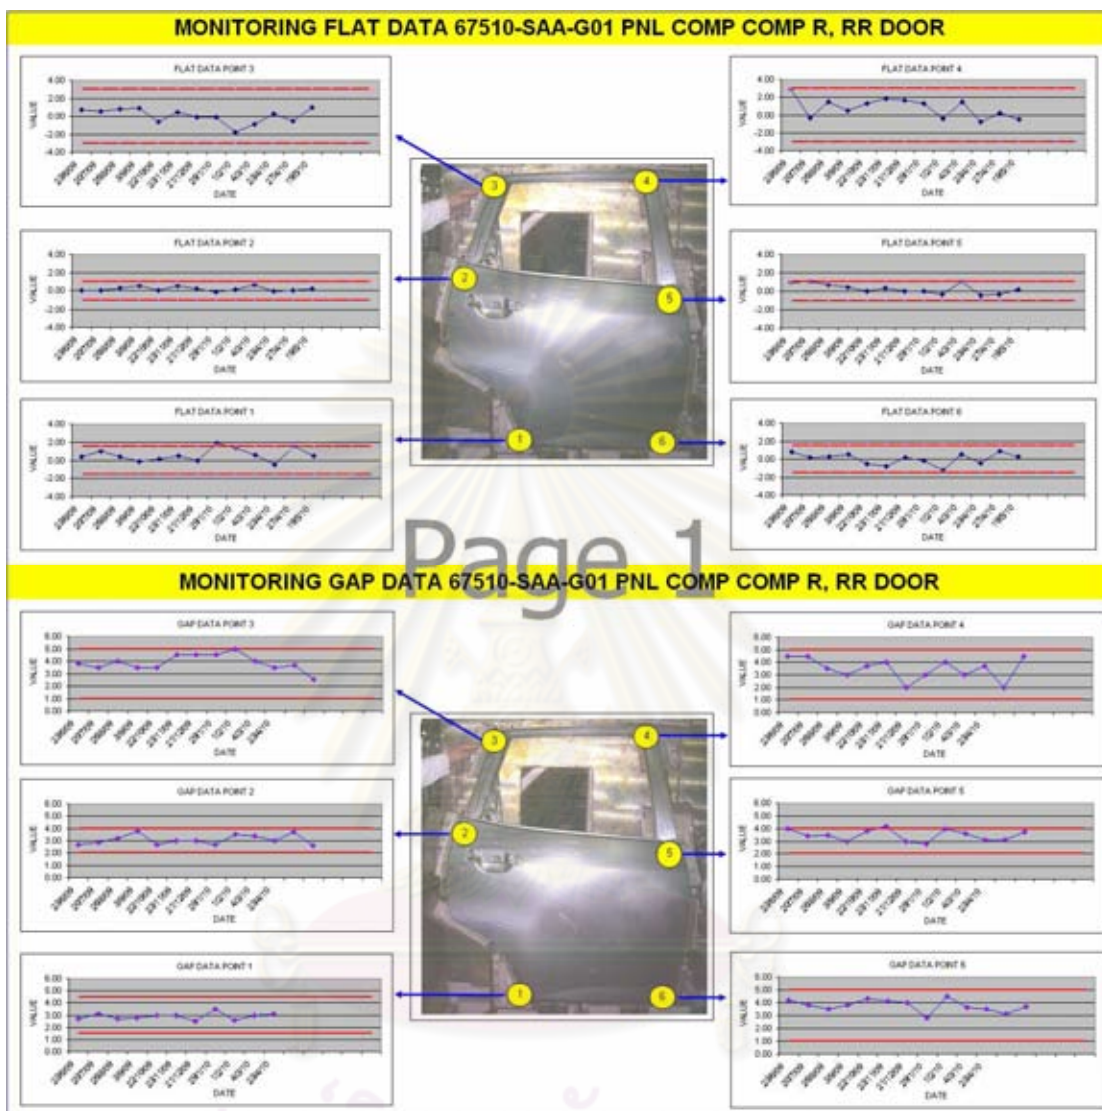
Data Check Sheet by Inspection Jig ของประตูหลังขวา
